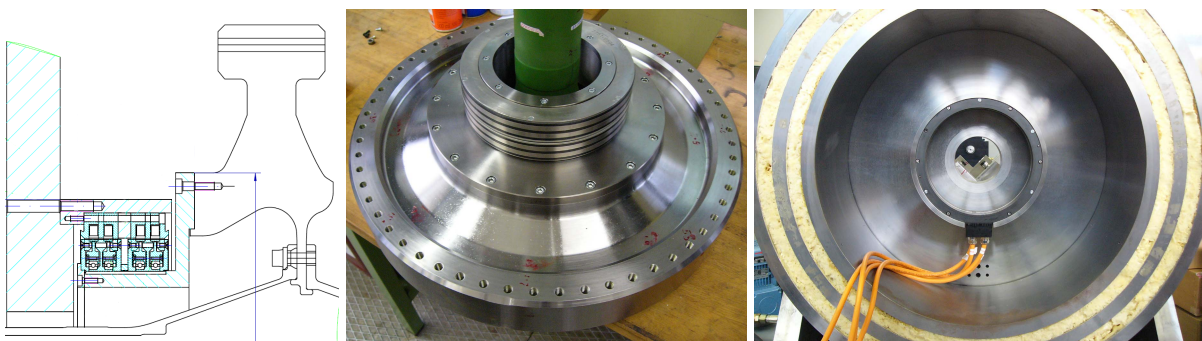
Aktives Auswuchtsystem (Balancer): Flansch, Mitte: Rotoren, Rechts: Statoren
